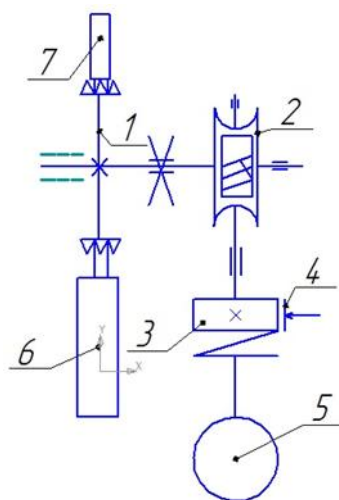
Расчетная кинематическая схема лифта с редукторной трансмиссией: 1 — КВШ; 2 — редуктор червячный; 3 — соединительная муфта с тормозным шкивом; 4 — колодочный тормоз; 5 — электродвигатель; 6 — кабина; 7 — противовес
